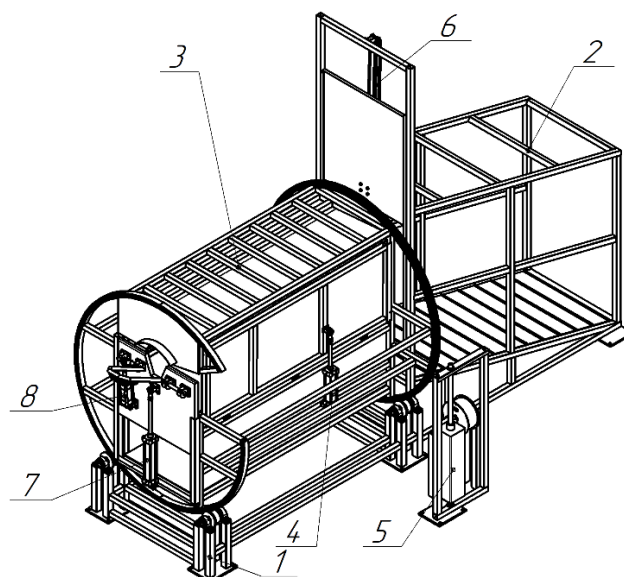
Общий вид установки: 1 – каркас; 2, 4, 5 – крышка; 3 – резервуар; 6 – узел приводной
